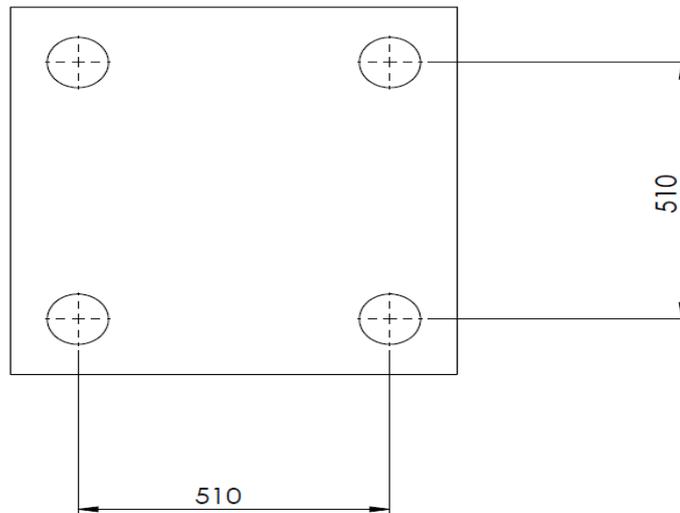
Schéma d'un plateau d'une presse 150T.
